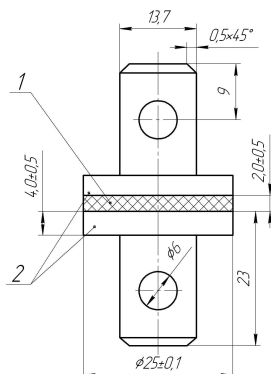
Форма образцов на испытание прочности связи при отрыве: 1 - образец резины, 2 - металлические диски
